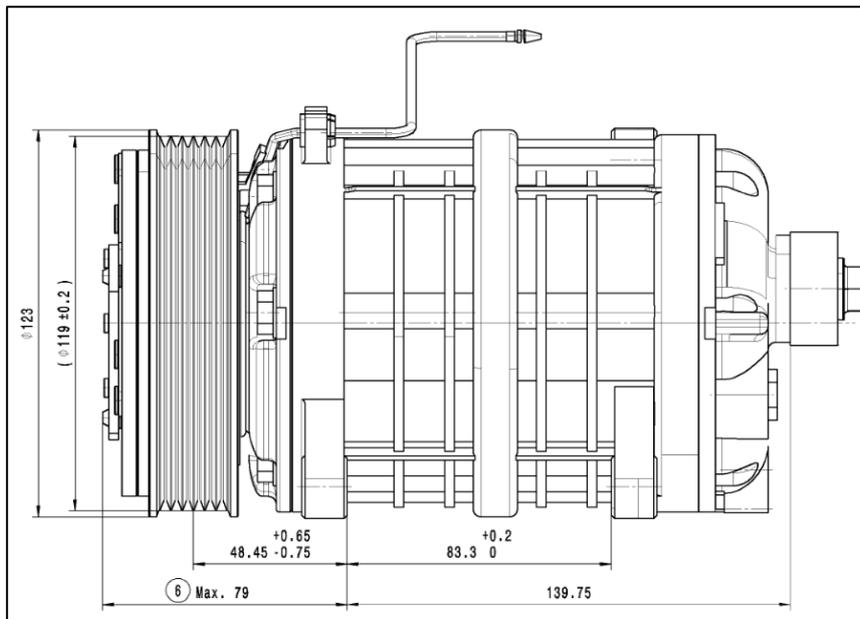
Dimensions du compresseur de climatiseur (7C0.816.803 D/E), vue de côté
